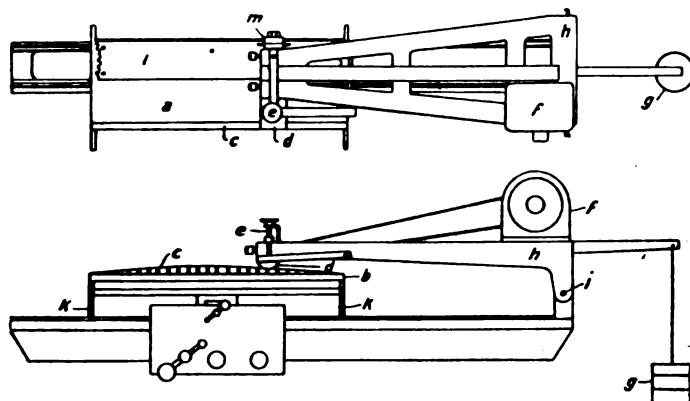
Schneidmaschine nach Abb. 8 zur Herstellung von Holzflügeln mit veränderlichem Profil. 1 Werkstück, a Unterlagplatte, b Messinghalter für die Mikrometerschrauben, c Blattfeder, d Führungsschuh, e Schraube zur senkrechten Einstellung des Führungsschuhs, f Elektromotor, g Ausgleichsgewicht, h Rahmen, i Rahmenlagerung, k Schlittenführung.
